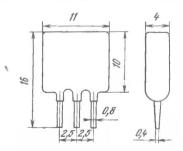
Габаритные и присоединительные размеры фильтров ФП1П8-62 и ФП1Р8-63
